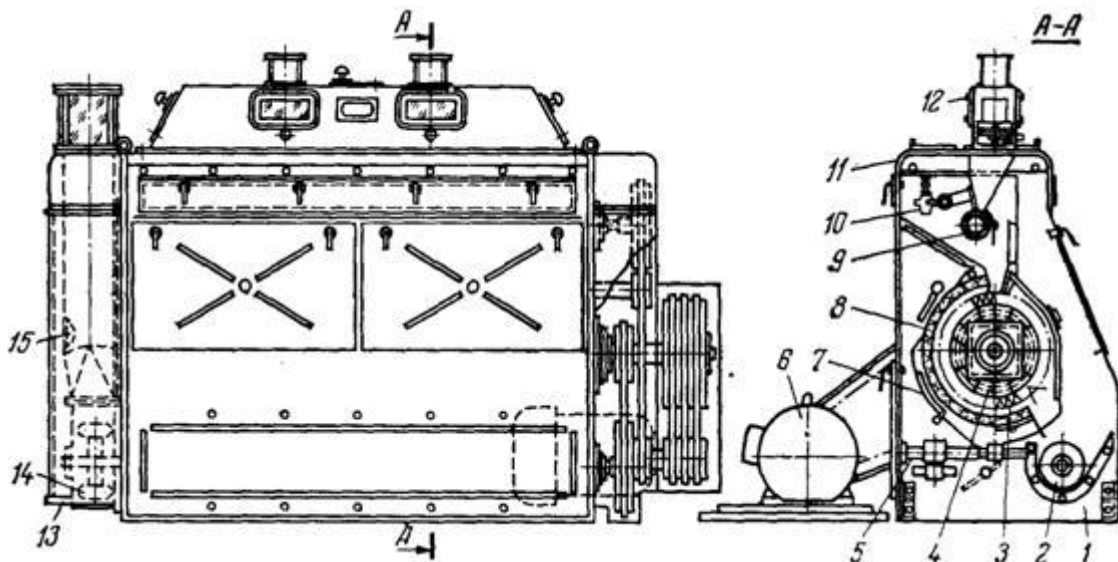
Щіткова машина типу БЩМ: 1 – корпус; 2 – шнек; 3 – рухлива щока; 4 – щітковий ротор; 5 – механізм для повороту деки; 6 – електродвигун; 7 – шкала з умовним таруванням; 8 – щіткова дека; 9 – живильний валик; 10 – механізм для регулювання рівномірності зерна, що надходить; 11 – кришка корпусу; 12 – живильний пристрій; 13 – нижнє вікно корпусу збудника; 14 – збудник; 15 – продуктопровід.
